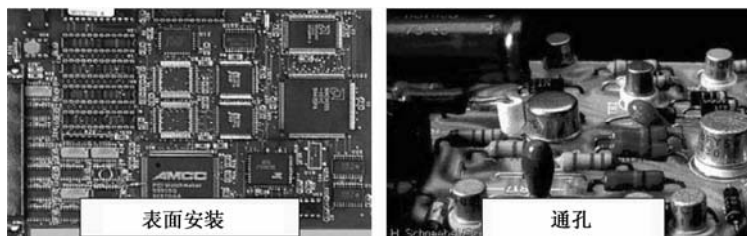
SMT 工艺和插件工艺的 PCBA 布局
